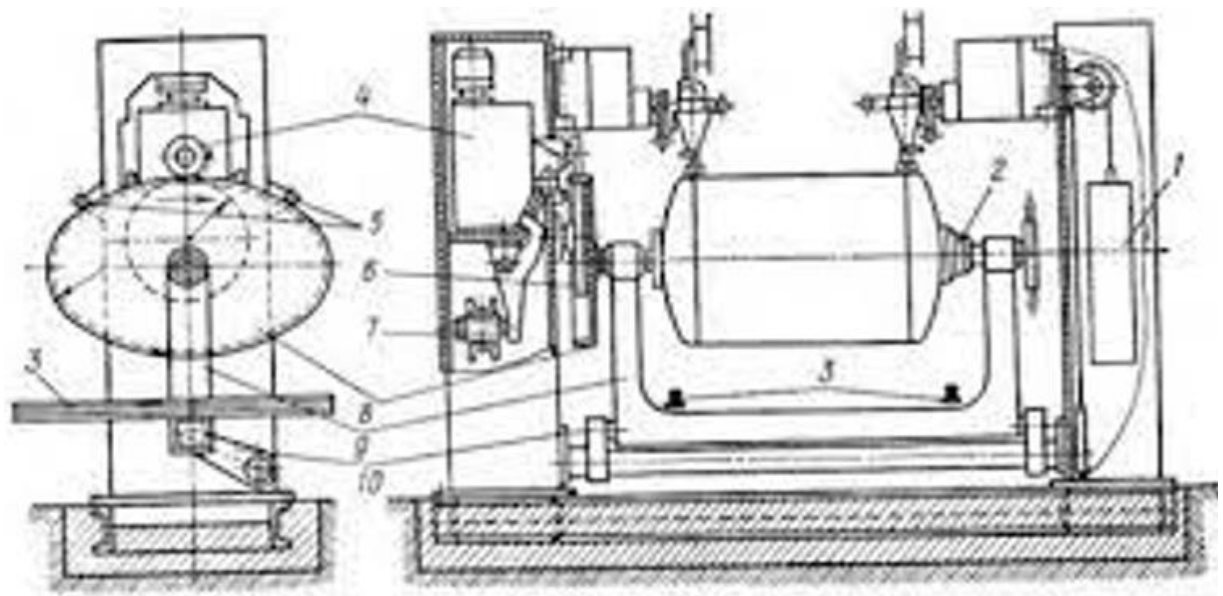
Установка для автоматического зварювання овальних посудин.
